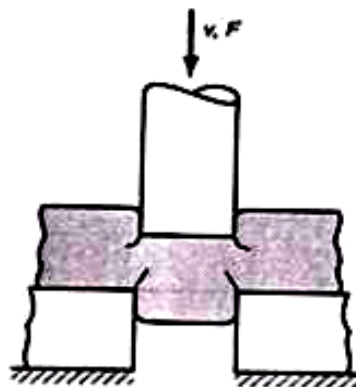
Un claro demasiado pequeño ocasiona una fractura poco óptima y se requieren fuerzas excesivas para llevar a cabo el proceso^{xxix}.
